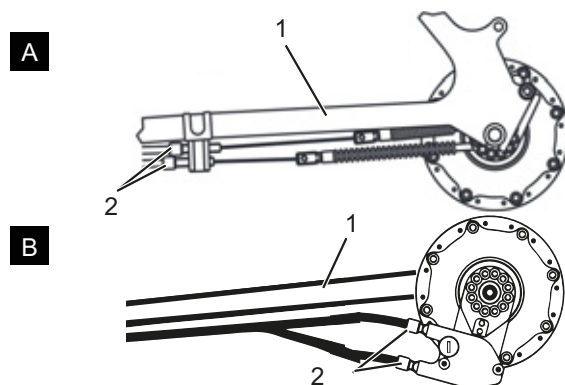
Slutmuffe (1) på gearskiftet med ét kabel og gearvælgerhus (2), eksempel
